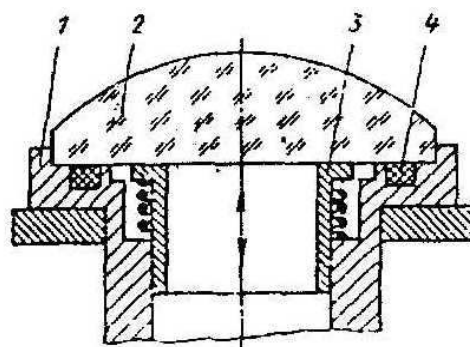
Пристосування для обробки торців заготовки не круглої форми
